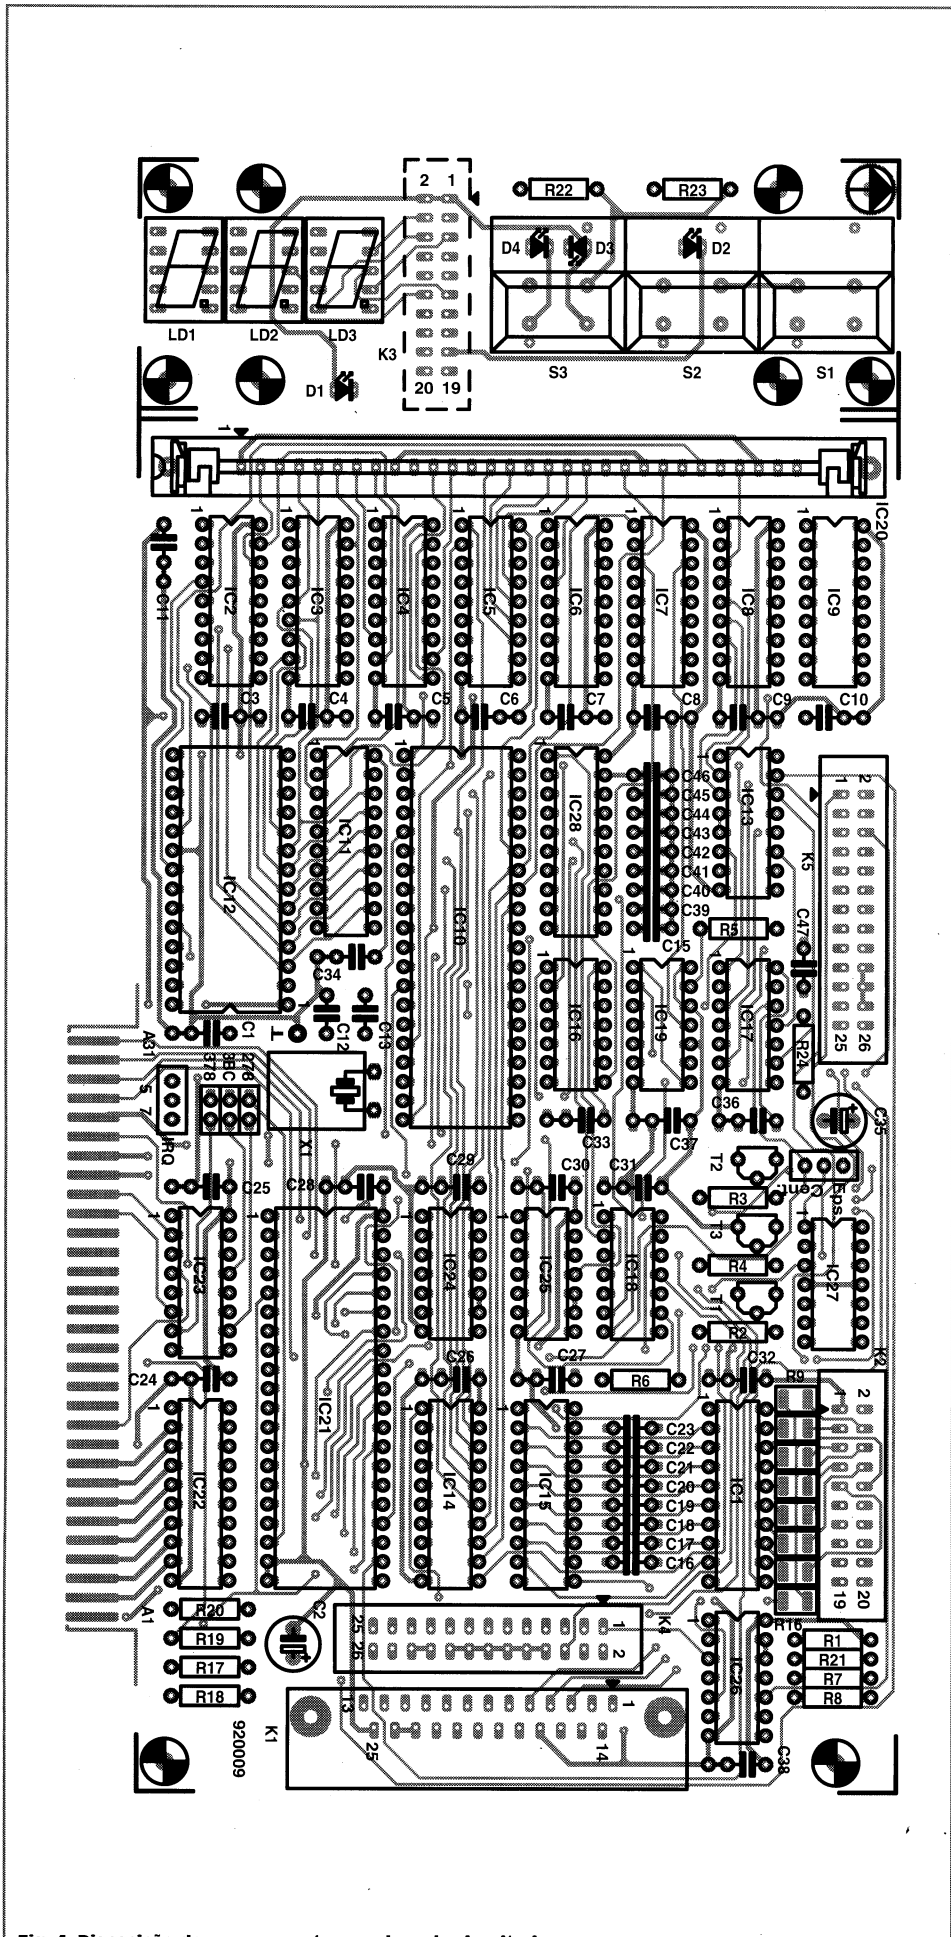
Disposição dos componentes na placa de circuito impresso.
